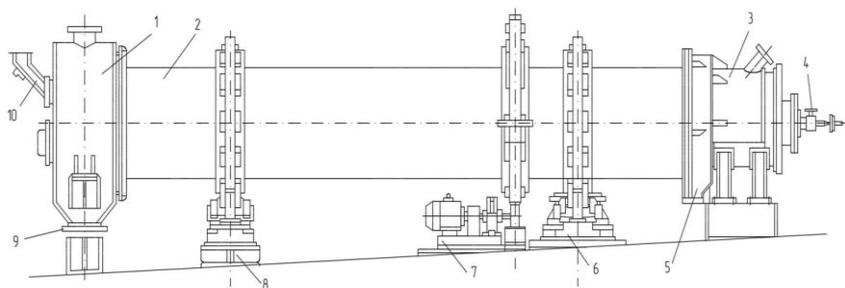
Печь для термоподготовки СМТ-178А:
